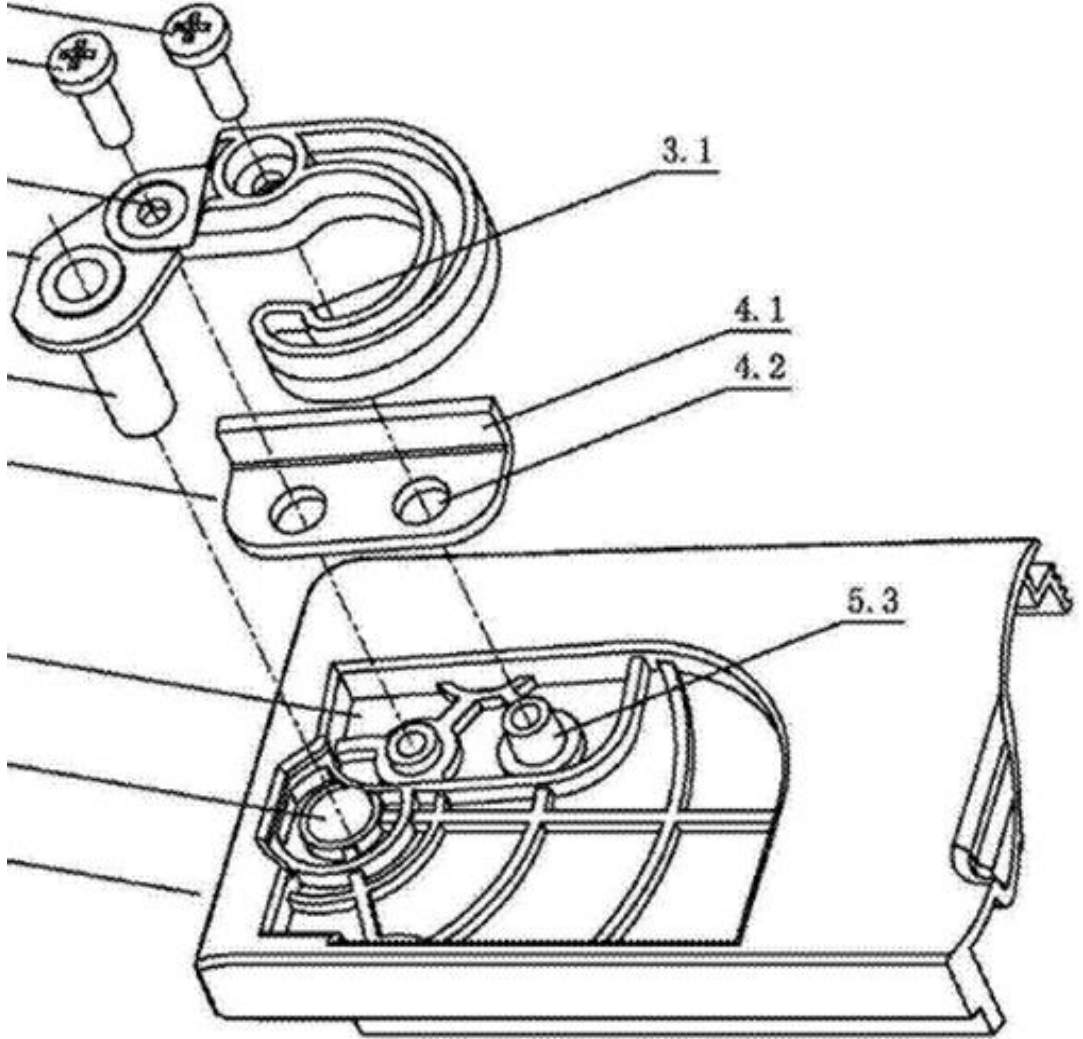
Blok halinde destek parçası montaj edilmiş çözüm [8].
